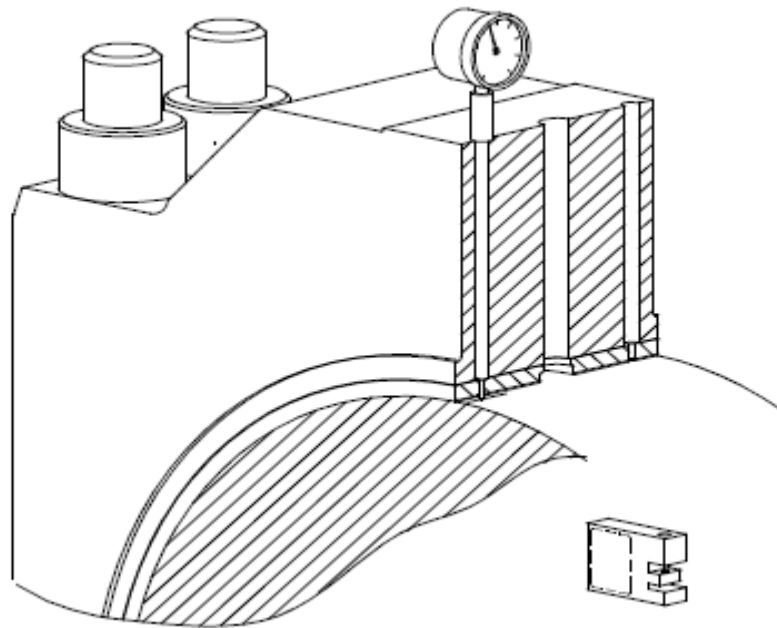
Вимірювання зазору в рамовому підшипнику індикатором
